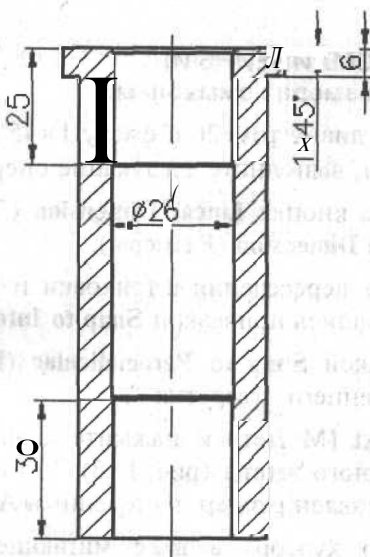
Чертеж втулки после нанесения линейных размеров без допусков
